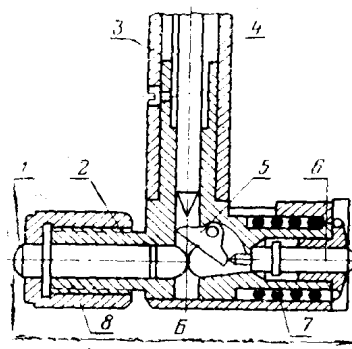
Корпус индикаторного нутромера с рычажной передачей и вставными стержнями: 1 – сменный стержень; 2 – втулка; 3 – трубка; 4 – стержень; 5 – двуплечий рычаг; 6 – подвижный стержень; 7 – пружина; 8 – гайка
